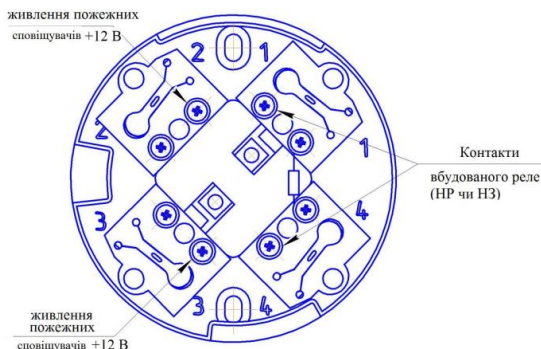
Розетка сповіщувача ИПК-9. Загальний вигляд і розташування контактів
